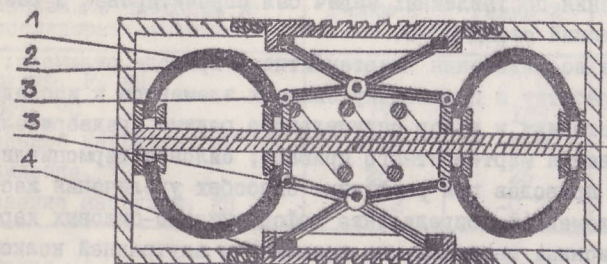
Конструктивная схема упорного устройства с коробчатыми упорами.
